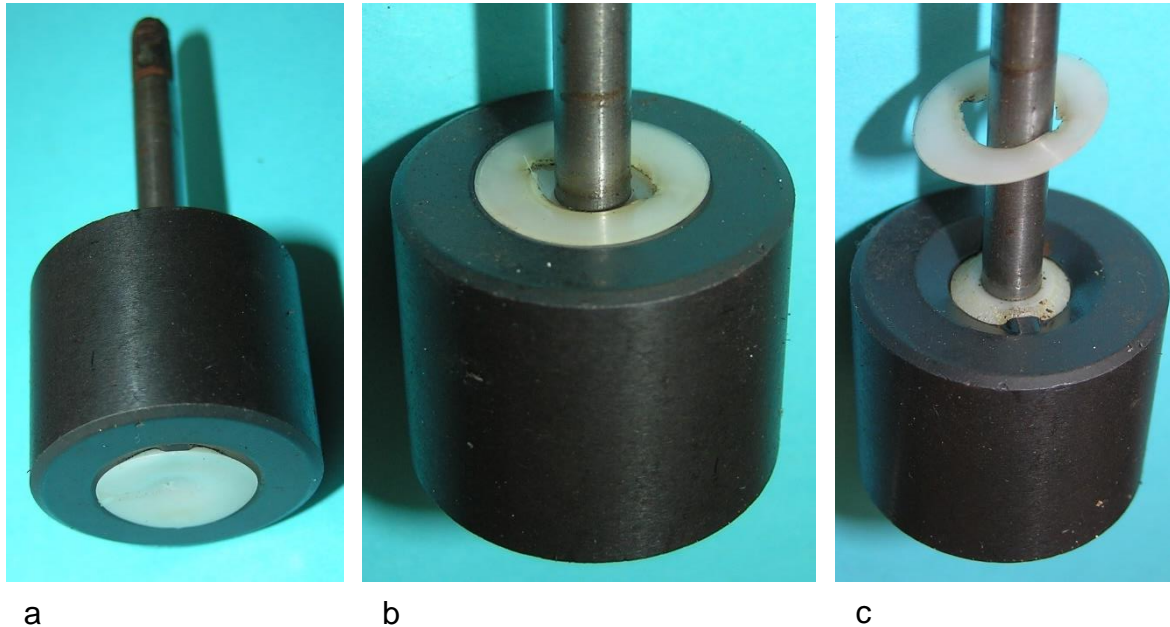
Ansichten des keramischen Polrads, Durchmesser 26 mm, Länge 22 mm
